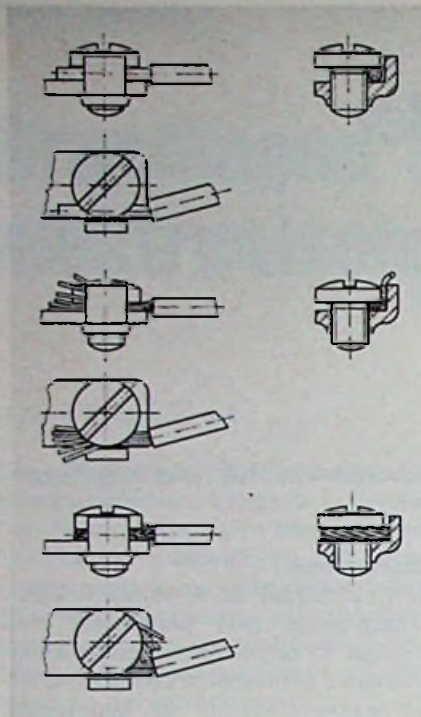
Drahtanschlüsse mit Schraubenkopfklemmen. Ohne Klemmplatte ist diese Klemmart hauptsächlich für Volldrähte geeignet. Litzen müssen verdrillt und zu einer Öse gebogen werden, weil sonst einzelne Drähte abspießen und einen Kurzschluß verursachen können.
